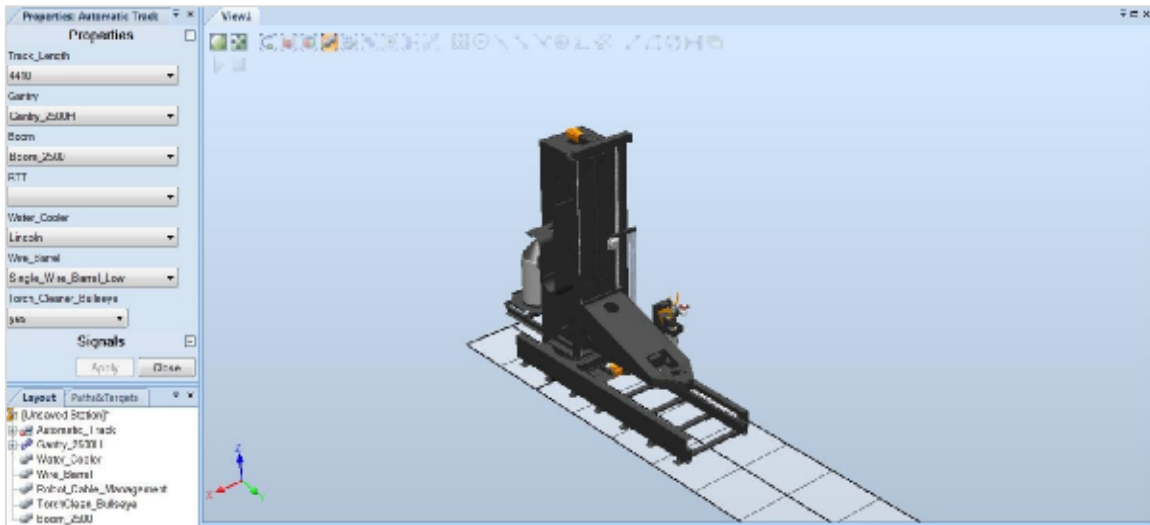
Розумний компонент Автоматичний конструктор доріжок
